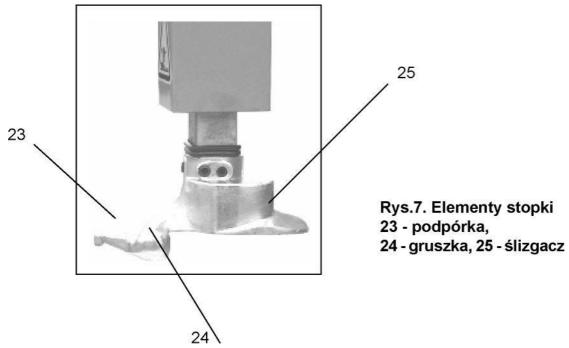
Элементы головки 23 – подпорка, 24 – груша, 25 - лопатка
